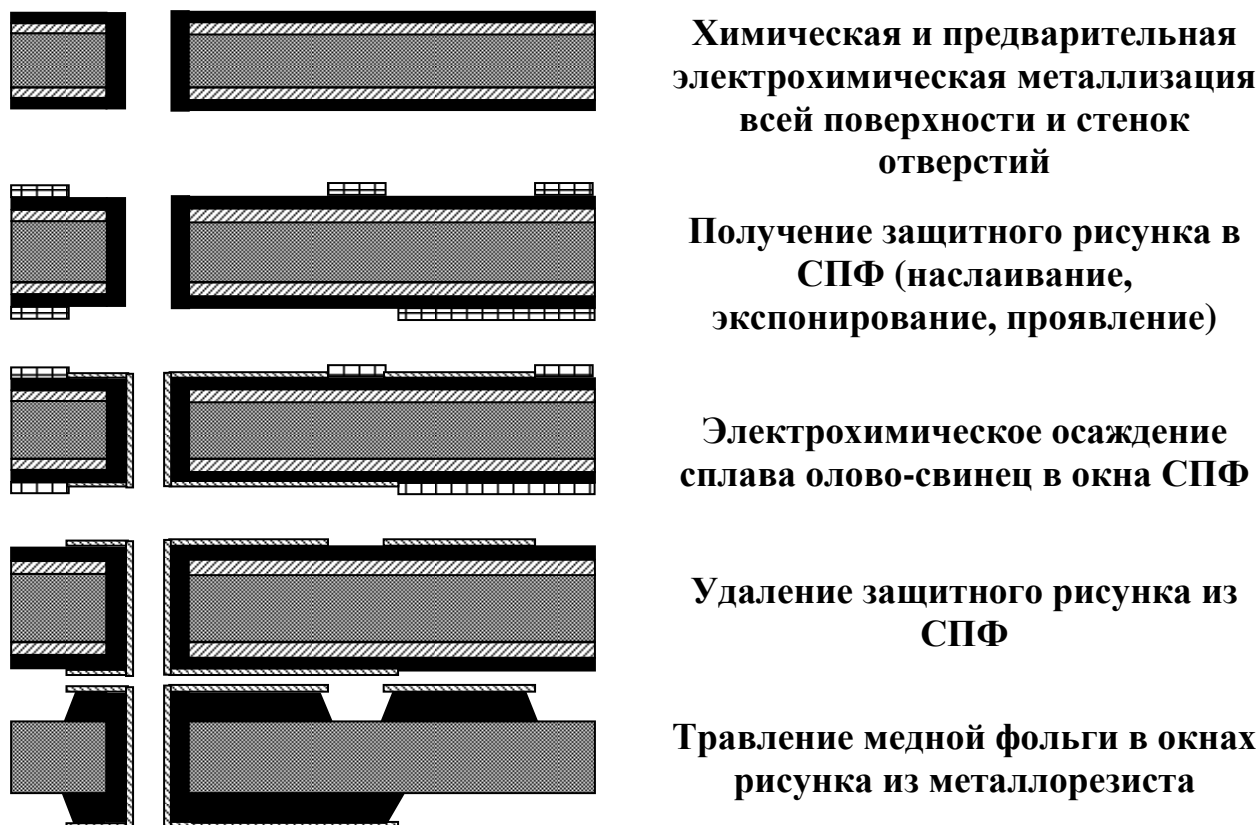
Изготовление слоев МПП субтрактивным позитивным методом с использованием металлорезиста олово-свинец
